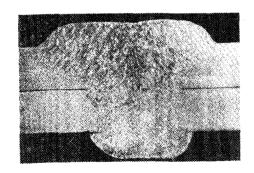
Макрошлиф соединения, выполненного дуговой точечной сваркой с принудительными сквозным проплавлением и формованием
